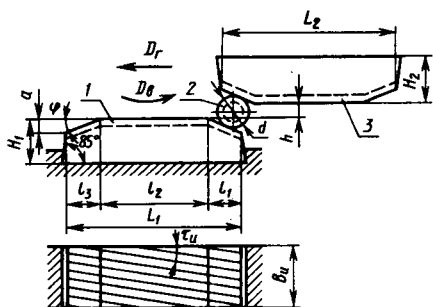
Схема образования резьбы резбо-накатными плашками
